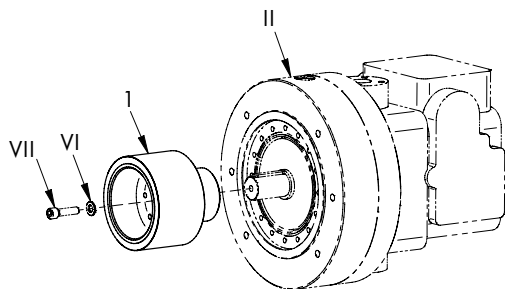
Montaggio del rotore interno lato di uscita (A1)
